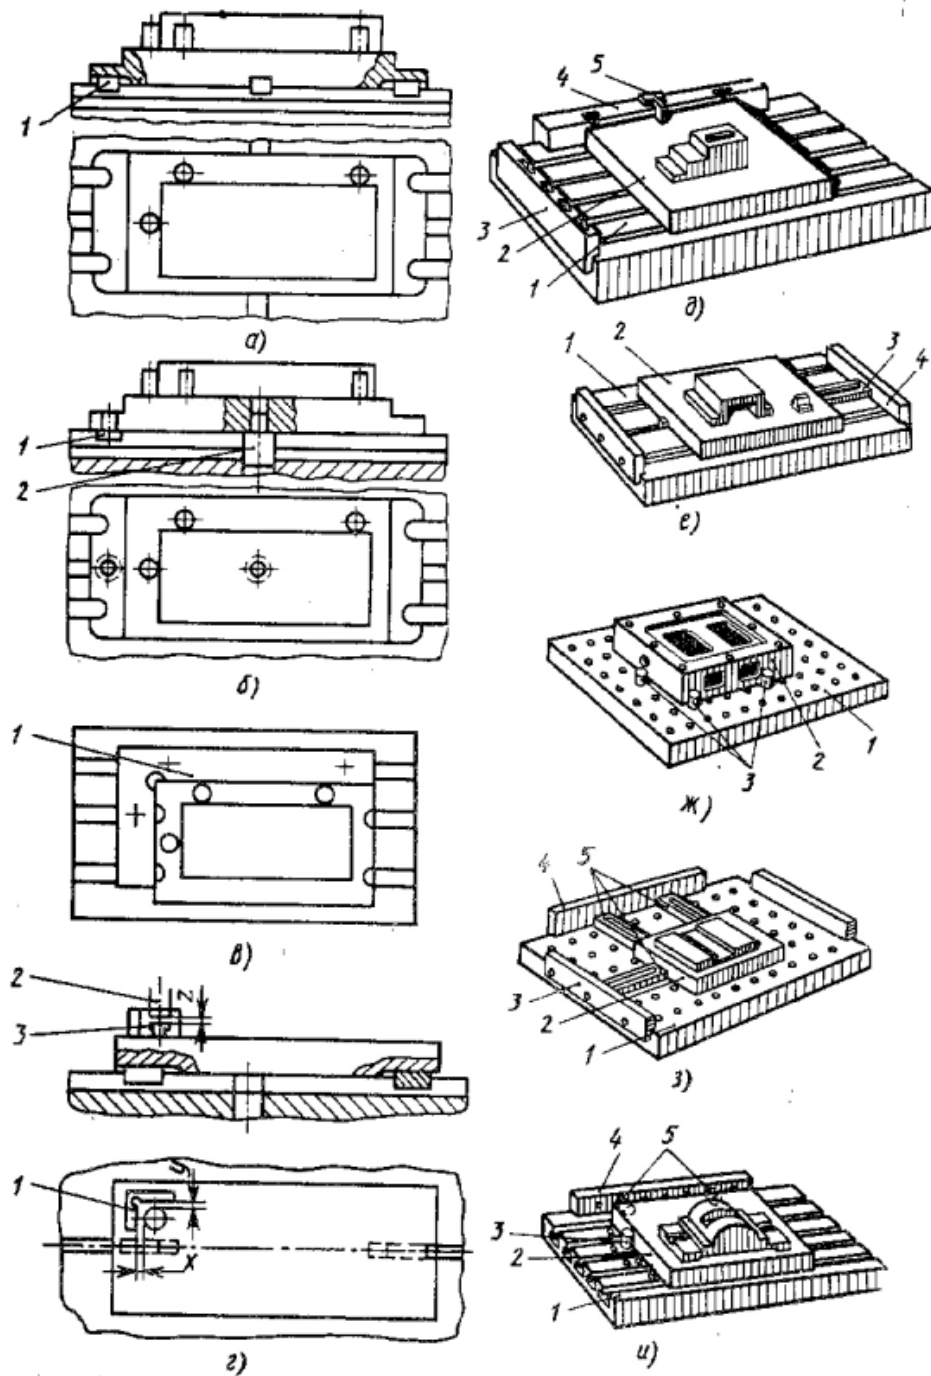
Схема базирования приспособления с помощью станка: 1 – стол станка;
